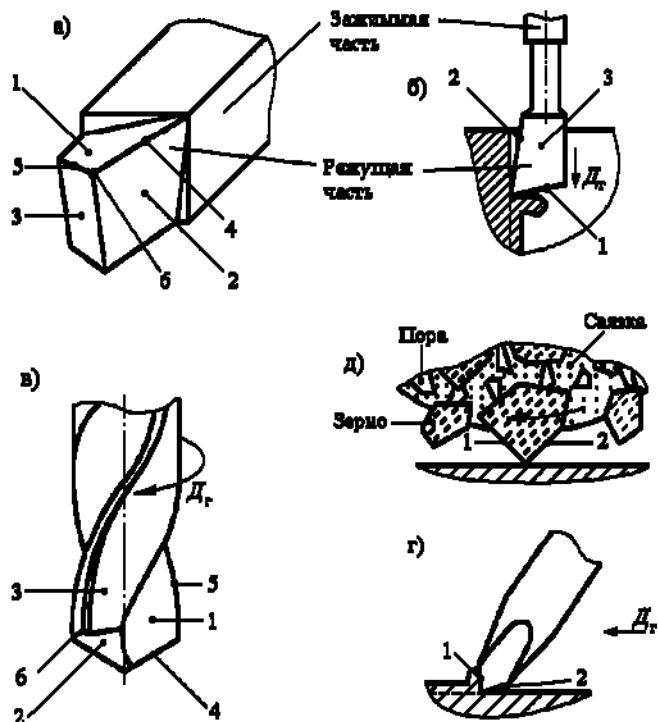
Составные части и рабочие поверхности инструментов (а – токарного резца, б – долбежного резца, в – спирального сверла, г – слесарного зубила, д – зерен абразивного инструмента):
